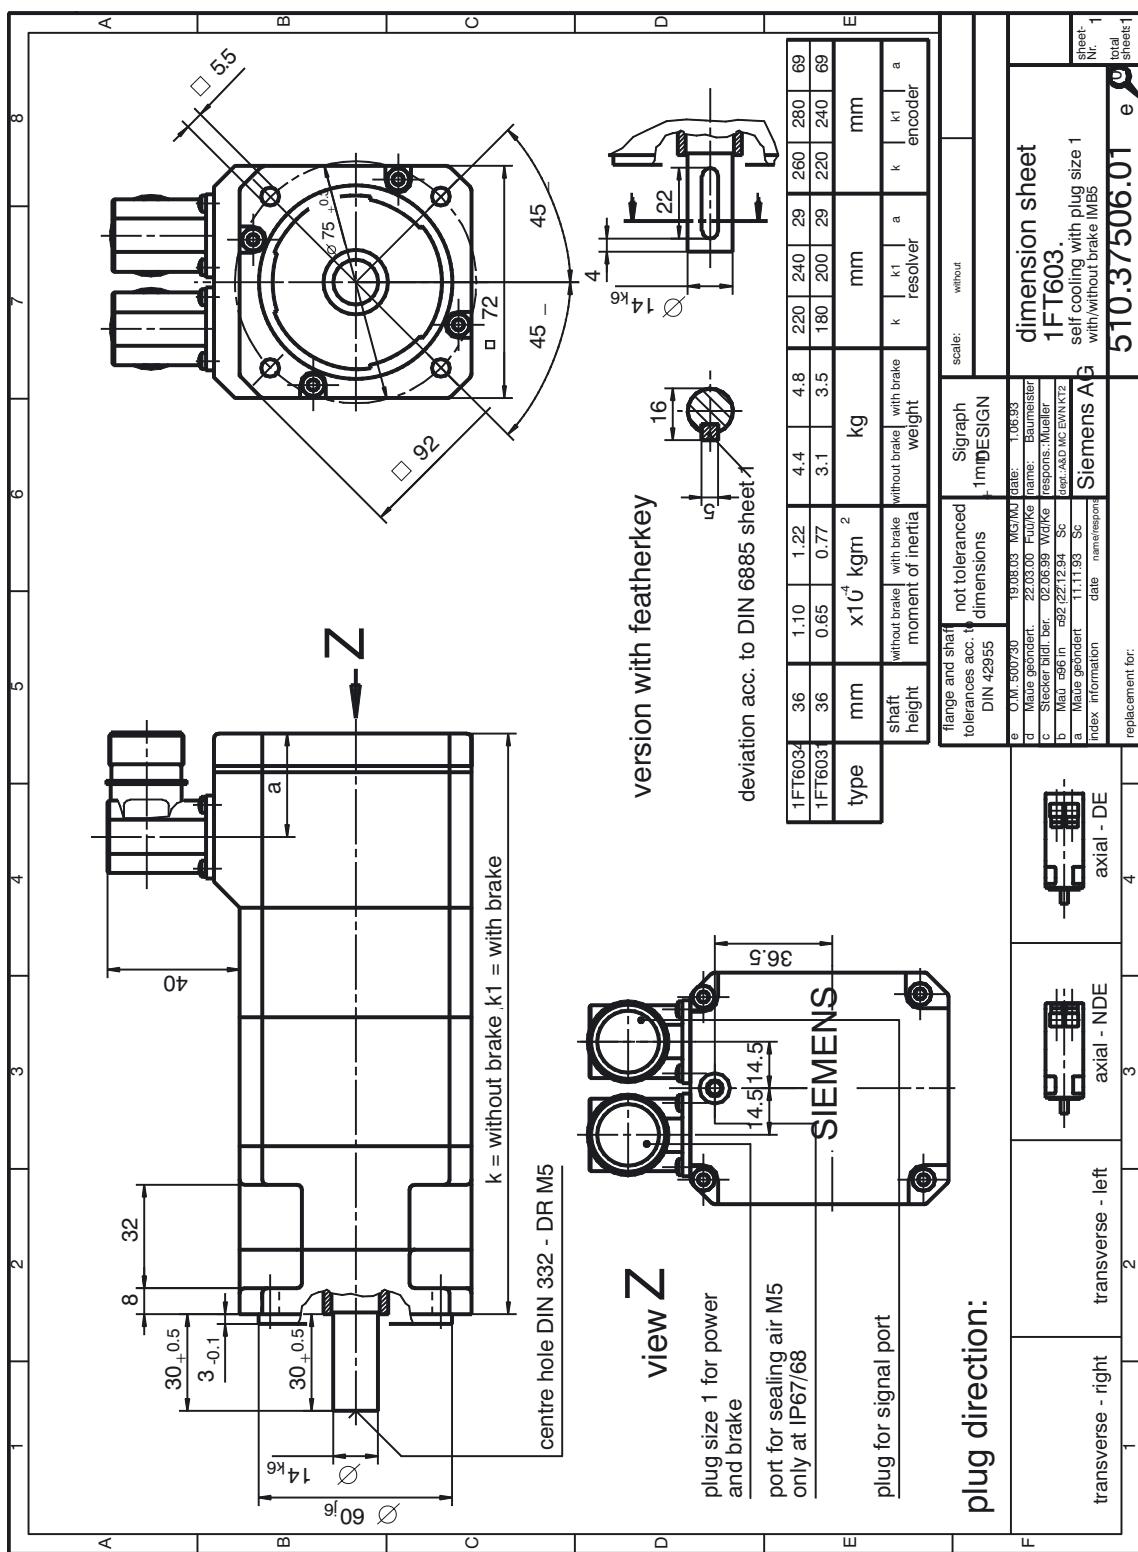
1FT603□ selbstgekühlt mit Stecker Größe 1
